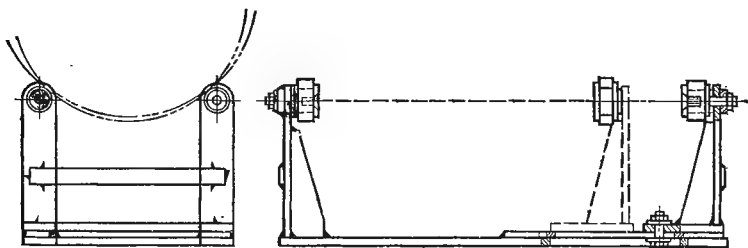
Роликовое приспособление для поворота ремонтируемой машины вокруг горизонтальной оси
